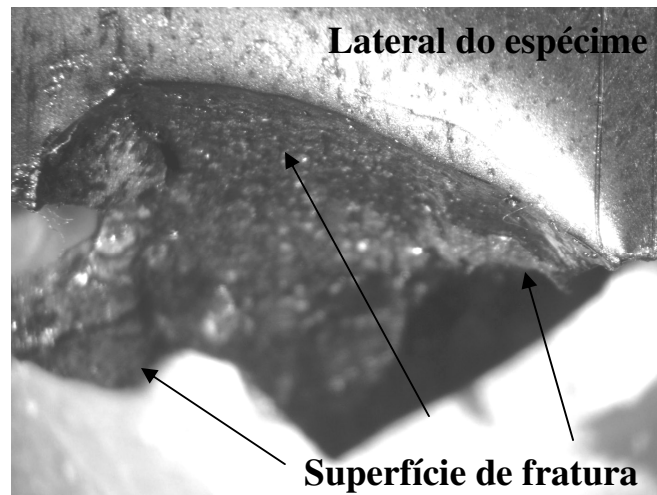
Vista perpendicular à superfície de fratura de espécime SE(T) com trinca profunda, sem entalhe lateral, CTP01-SE-V
